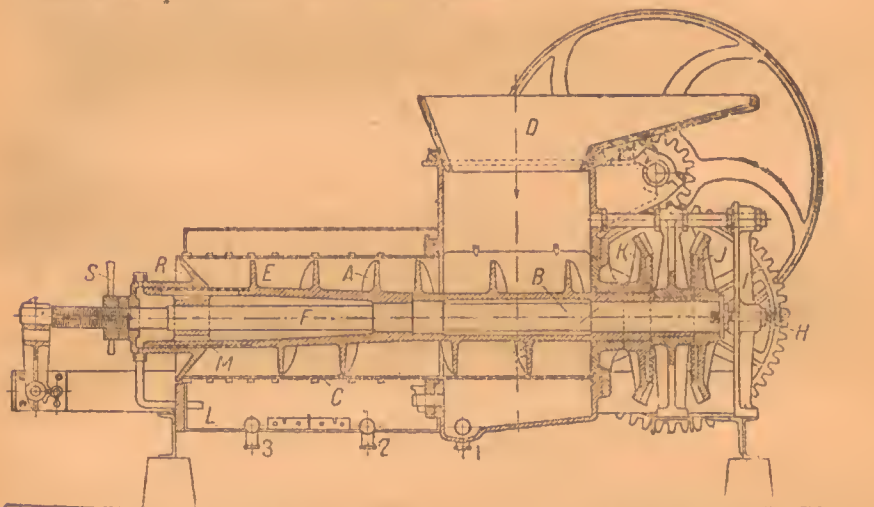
Детали конструкции пресса непрерывного действия Колена.
